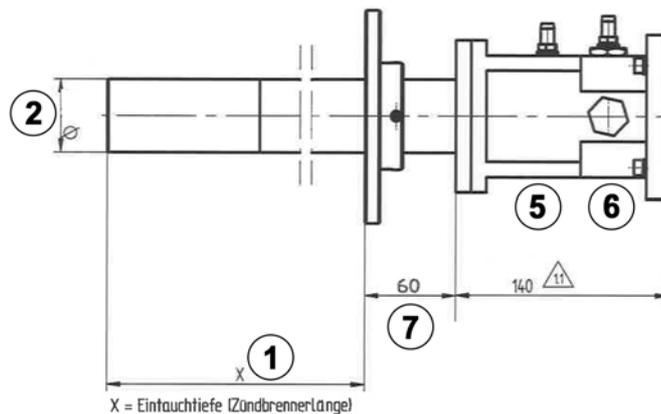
Dimensiones del quemador de ignición GFI48, variante C
